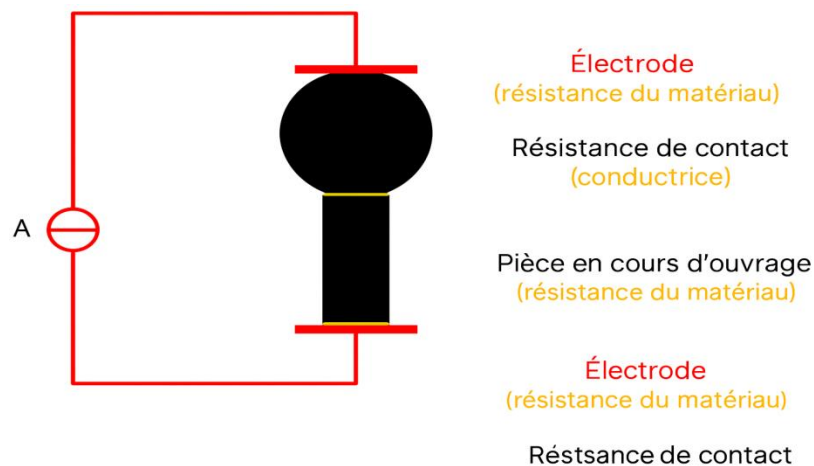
Exemple de modèle pour un procédé de soudage par résistance
